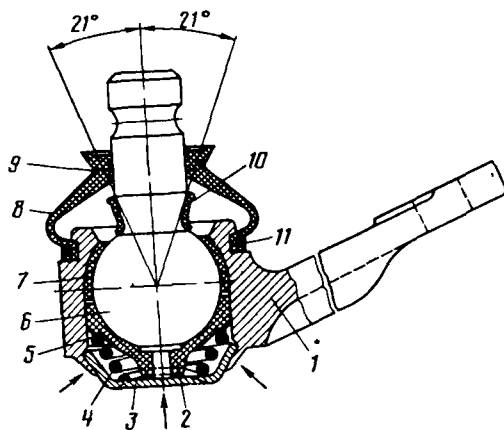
Шаровой шарнир стойки передней подвески: 1 — корпус; 2 — нижний вкладыш; 3 — заглушка; 4 — пружина; 5 — упорная шайба; 6 — шаровой палец; 7 — верхний вкладыш; 8 — защитный чехол; 9 — обжимное кольцо; 10 — защитный вкладыш; 11 — хомут; Стрелками показаны посадки при выборе люфта
